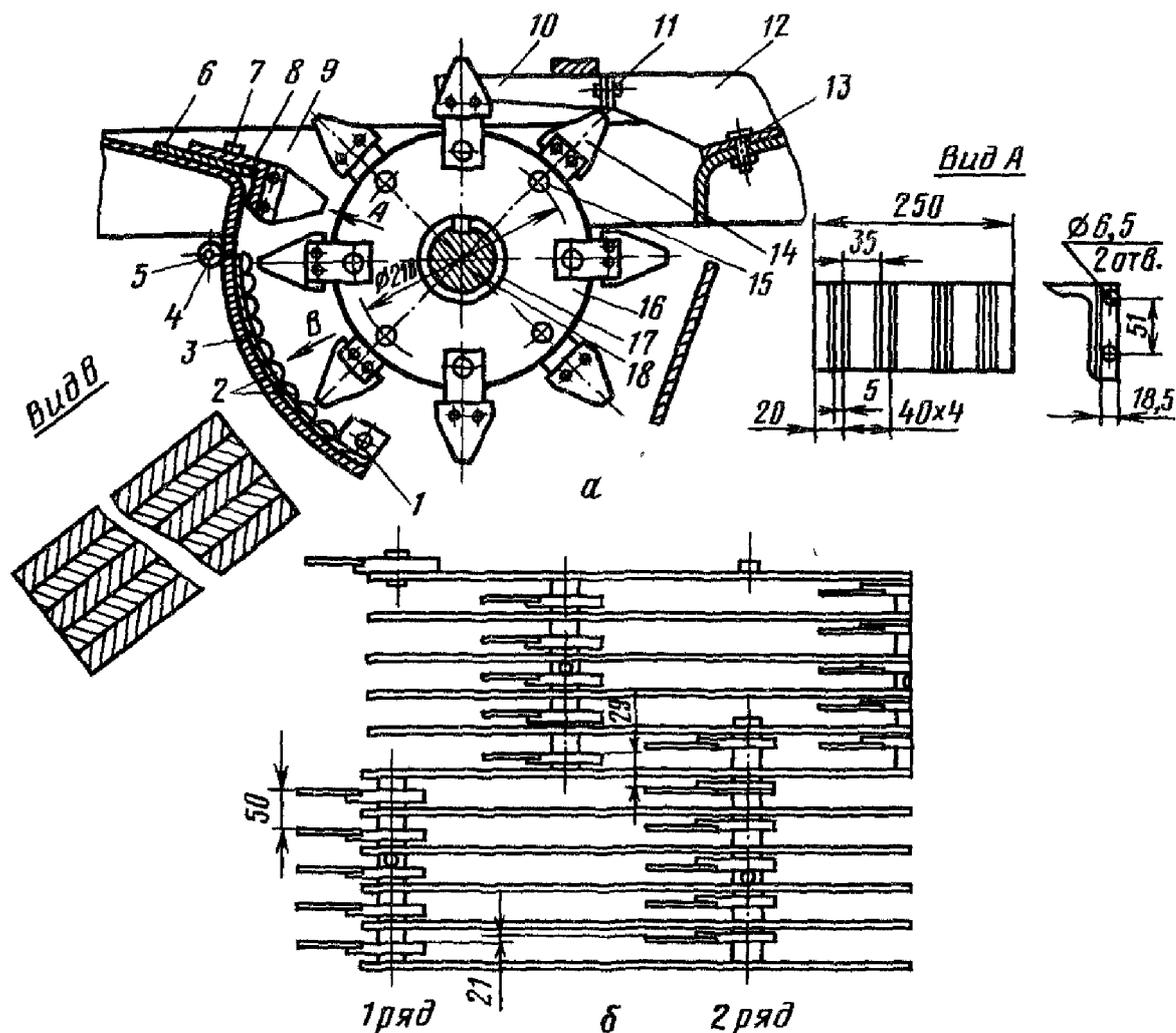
Схема модернизированного измельчающего аппарата ИРТ-165 (а) и схема расположения деталей ротора (б):
